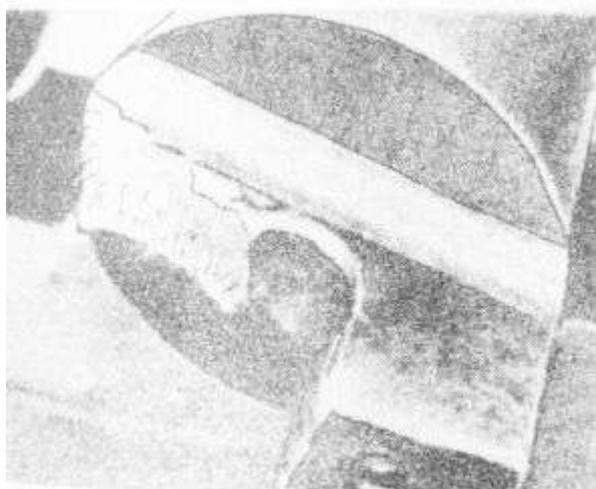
Усталостный излом шейки станинного ролика стана 4500
